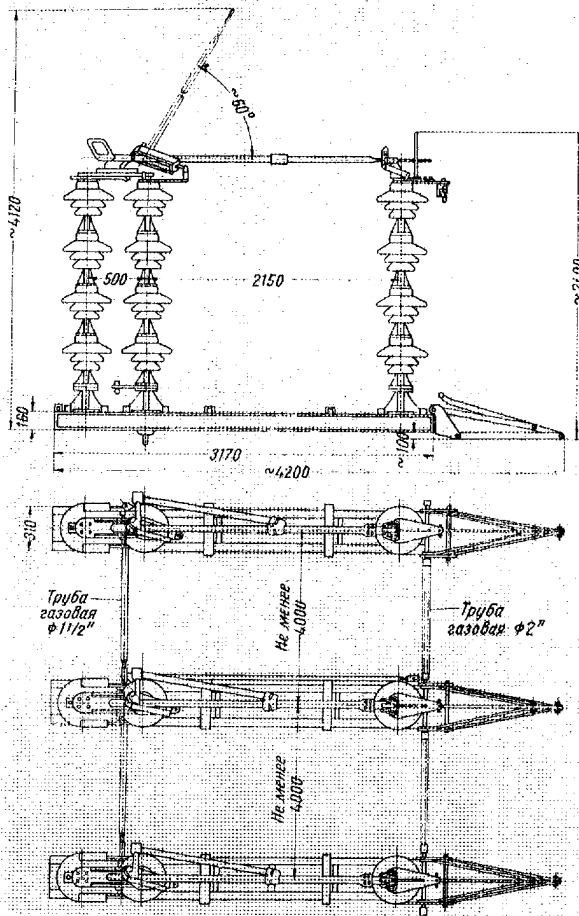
Габаритный эскиз разъединителя РЛНЗ-154.
